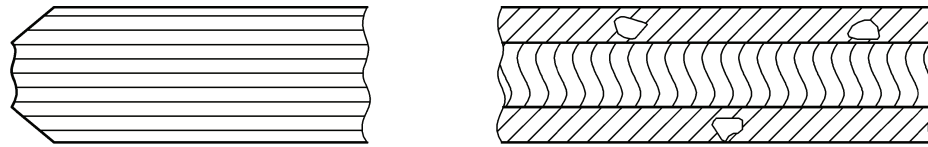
Gesäumte Kante (mit blanken Stellen)
